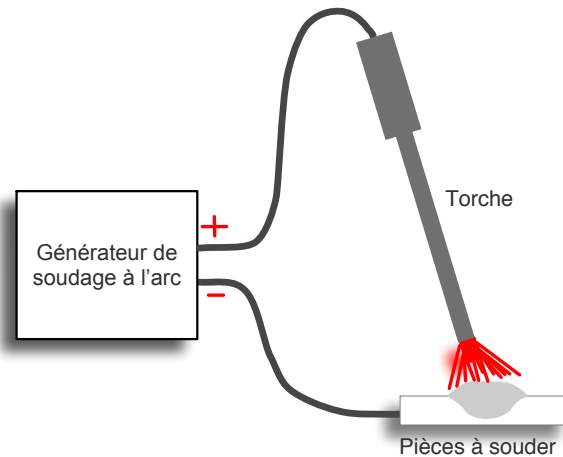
Circuit électrique d'un procédé de soudage
